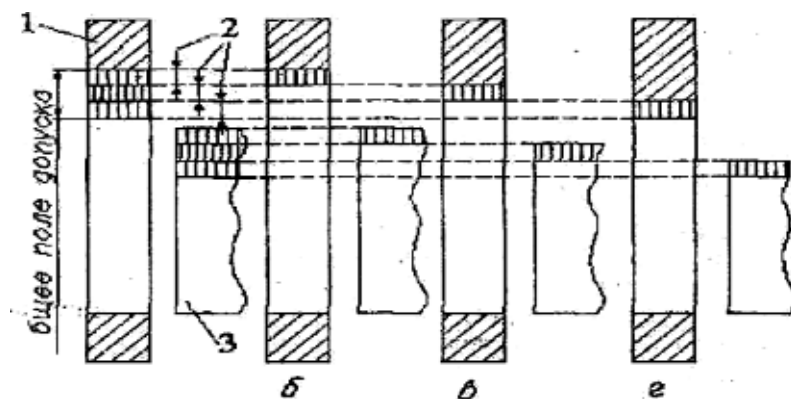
Схема селективного подбора двух соединённых деталей: *а* — разделение полей допусков на интервалы; *б... в* - подбор соединённых деталей по размерным группам; 1 и 3 - охватывающая и охватываемая детали; 2 - интервалы полей допусков
